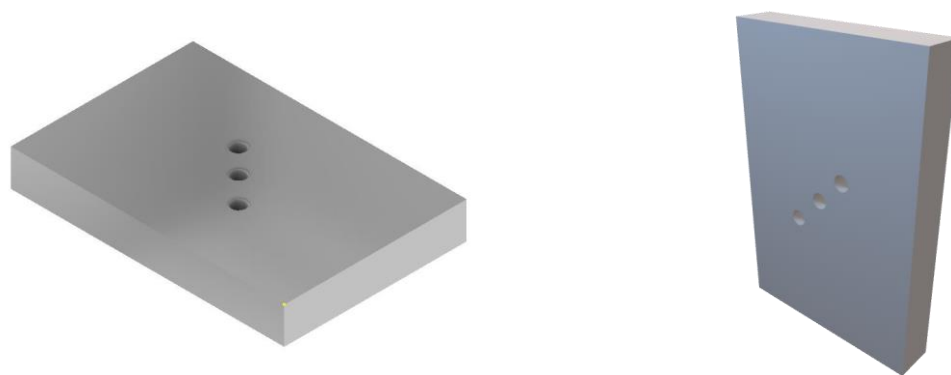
Τρισδιάστατη απεικόνιση αποστολής 21
